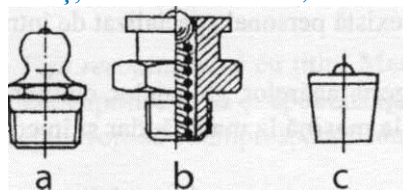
Ungător cu bilă: a - cu cap sferic și filet conic; b - cu cap plat; c - cu cap plat fixat prin presare.
